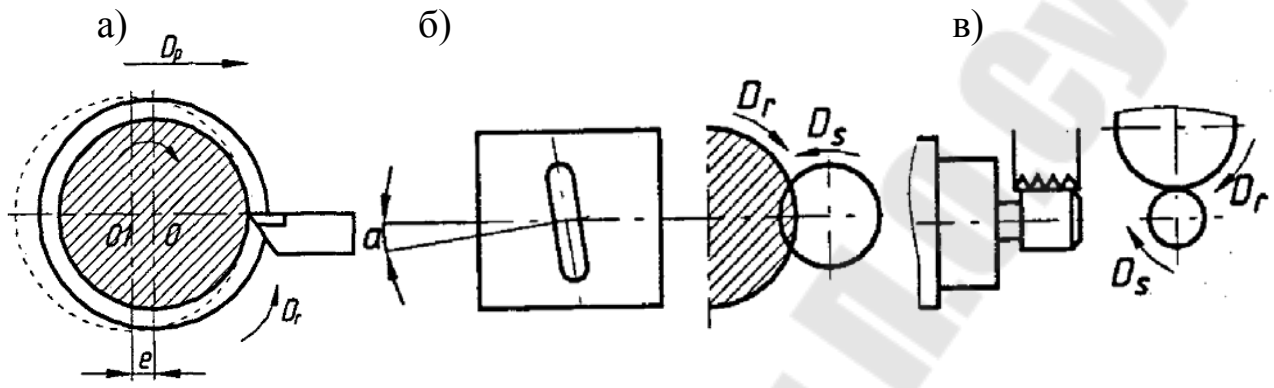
Схемы вихревого резьбонарезания (а) и фрезерования резьбы (б – дисковой фрезой, в – групповой (гребенчатой) фрезой)
